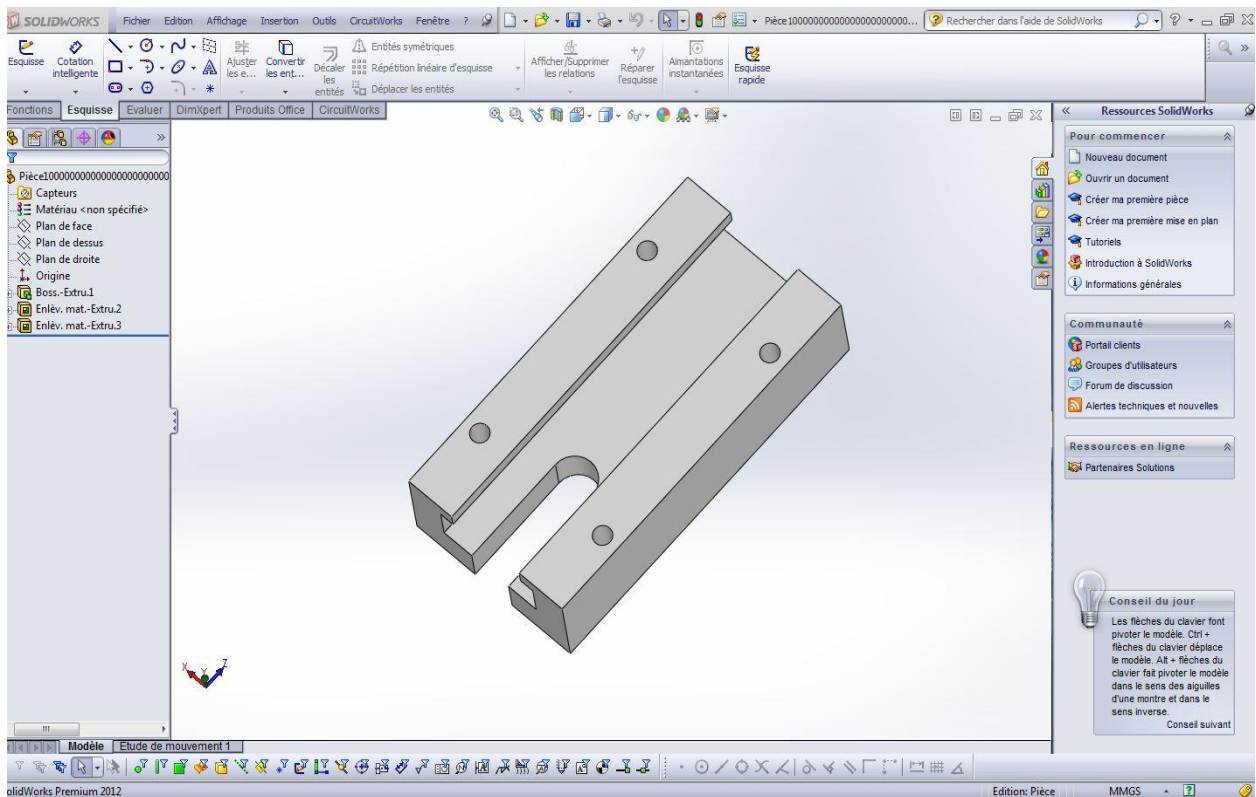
Vue Glissière réalisée sous SOLIDWORKS
